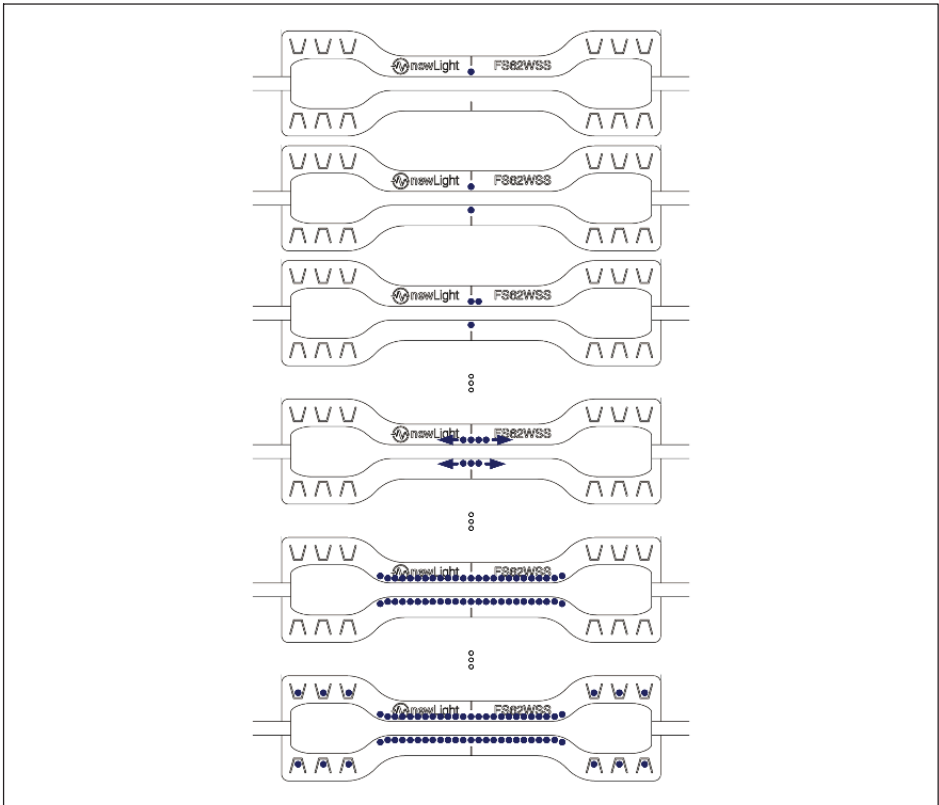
Schweißverfahren für FS62WSS
